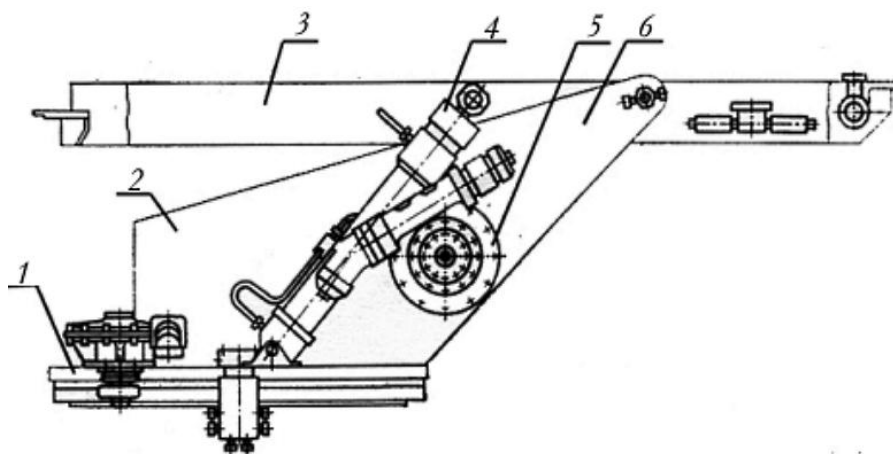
Підйомно-поворотний пристрій АД-30 (131) ПМ-506:
